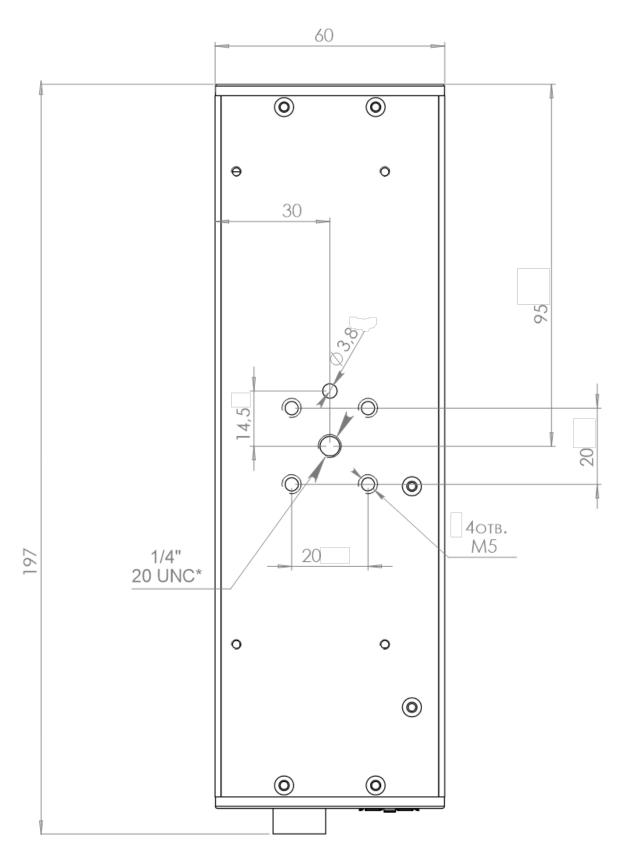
Габаритные размеры пирометра. Вид снизу.
